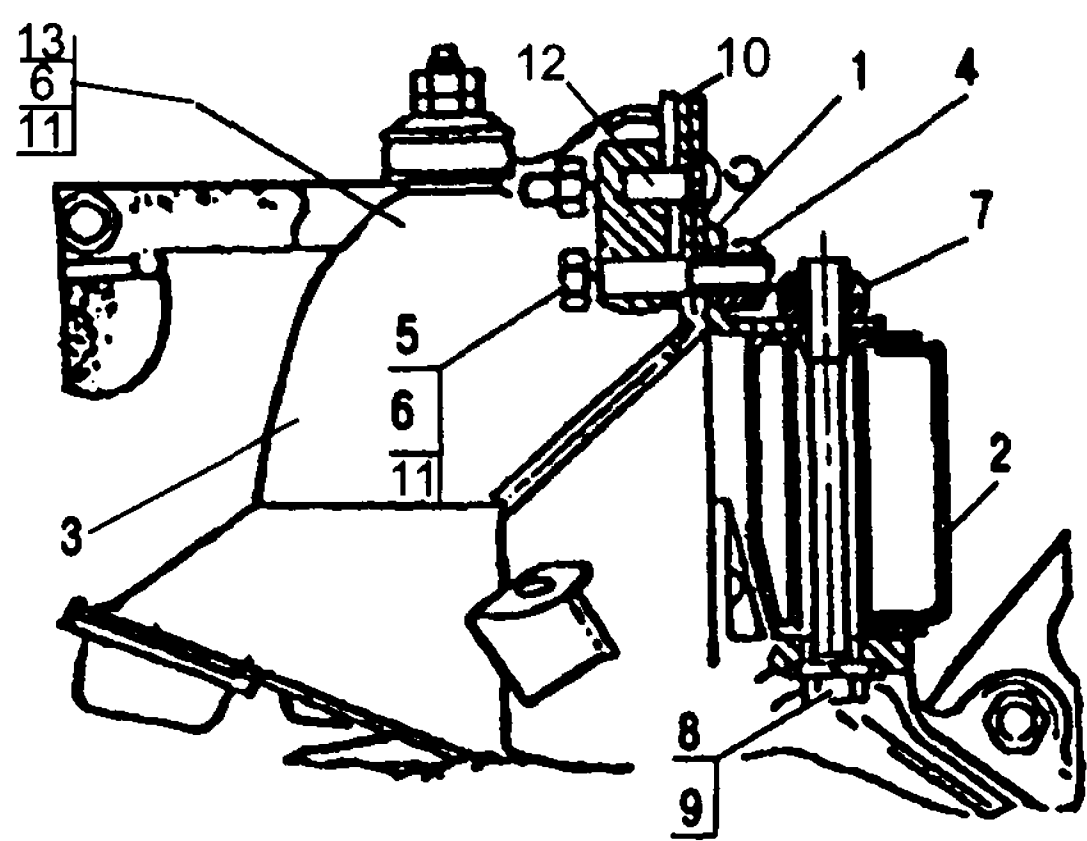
Крепление подвески к лонжерону: 1 - кронштейн; 2 - лонжерон; 3 - подвеска; 4 - планка горизонтального крепления; 5 - болт; 6 - шайба; 7 - планка вертикального крепления; 8 - болт; 9 - шайба; 10 - регулировочные прокладки; 11 - втулка дистанционная; 12 - ось верхних рычагов; 13 - болт с полукруглой головкой
